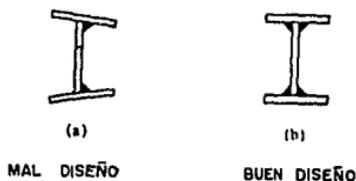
Efecto de la colocación de la Soldadura: (a) Mal diseño, (b) Buen diseño.
